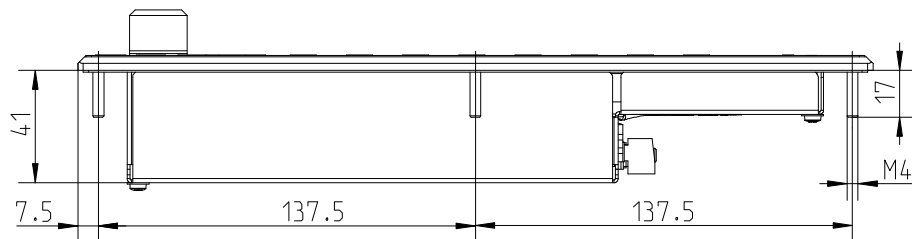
Abmessungen: Frontplatte des VDP 16.3DB
